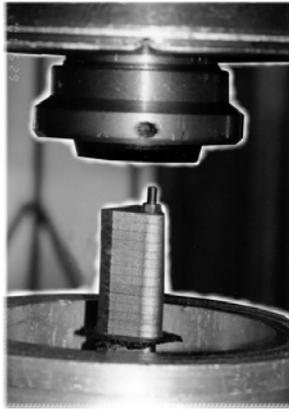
Рабочая зона станка “Дуга-8” при обработке пакета деталей
